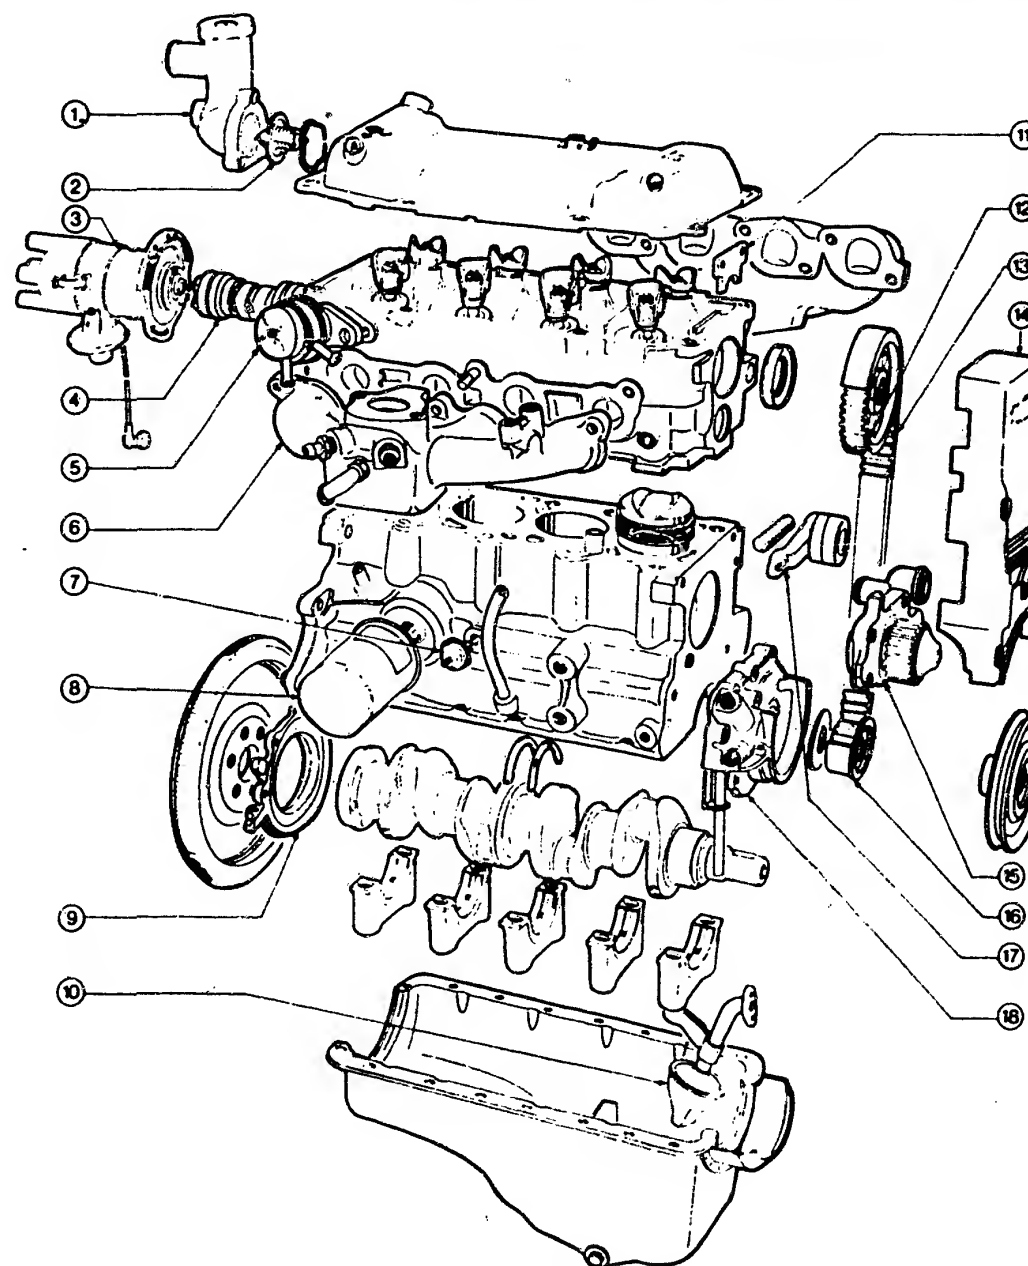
CVH-Motor zerlegt: 1 Wasserauslassstutzen – 2 Thermostat – 3 Zündverteiler – 4 Nockenwelle – 5 Kraftstoffpumpe – 6 Ansaugkrümmer – 7 Öldruckschalter – 8 Ölfilter – 9 Kurbelwellen-Dichtringträger – 10 Ölpumpensieb mit Saugrohr – 11 Nockenwellen-Halteplatte – 12 Nockenwellen-Zahnriemenrad – 13 Zahnriemen – 14 Zahnriemenabdeckung – 15 Wasserpumpe – 16 Kurbelwellen-Zahnriemenrad – 17 Zahnriemenspanner – 18 Ölpumpe.
